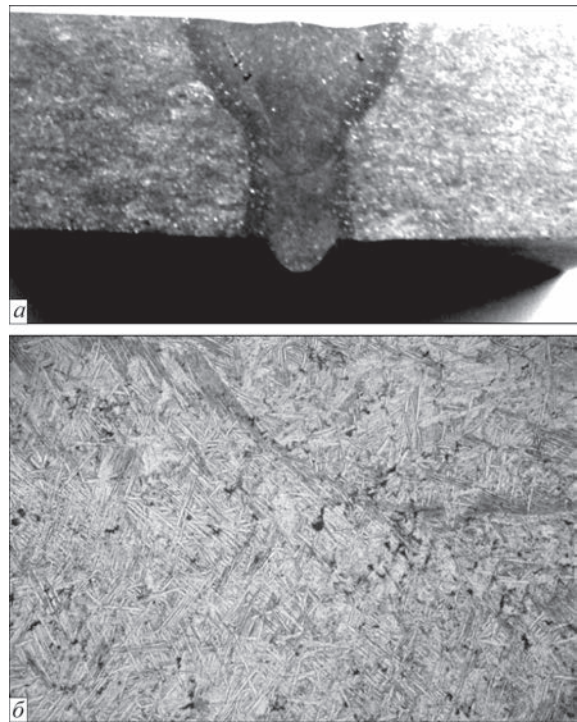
Структура образца № 2: а — поперечный макрошлиф сварного соединения; б — структура ЗТВ ( $\times 200$ )
